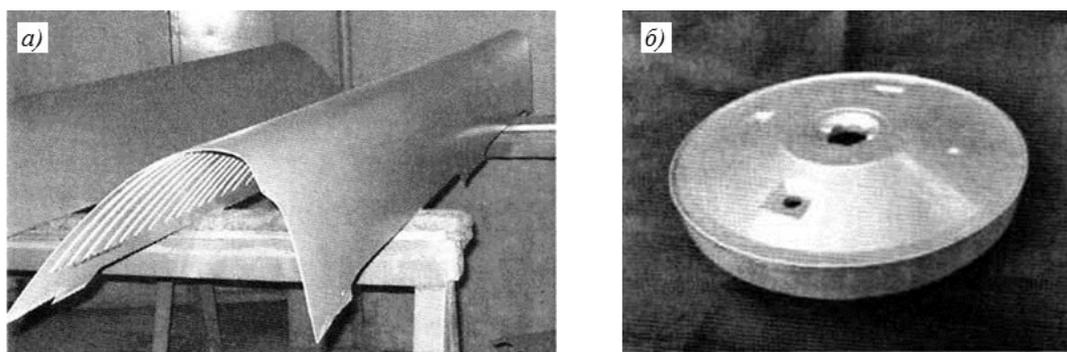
Элементы передней кромки крыла самолета Ан-148 (а) и сварной корпус гироскопа (б) из сплава 1370 [64]
